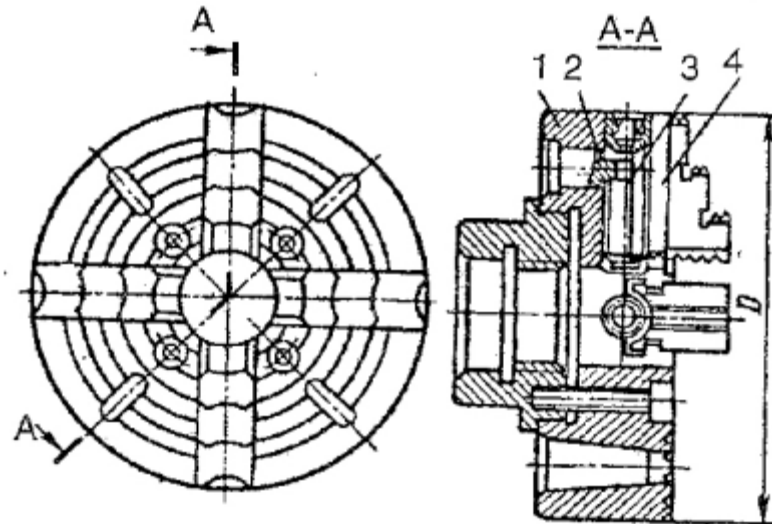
Конструкция четырехкулачкового патрона с независимым перемещением кулачков: 1 – корпус; 2 – сухарь; 3 – винт; 4 – кулачок.
